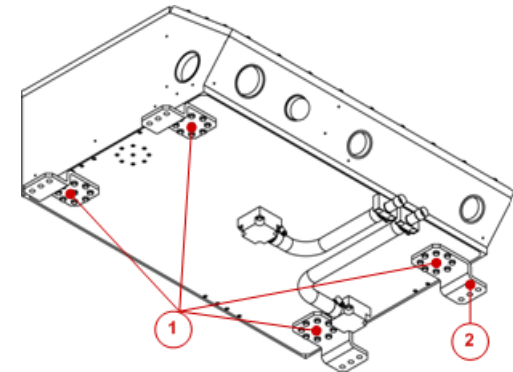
Befestigungswinkel VHC / VHC mounting bracket
